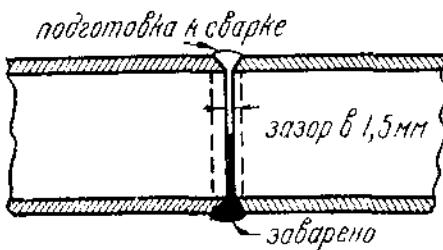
Сварка трубопроводовстык, заменяющий нормальное фланцевое соединение.
